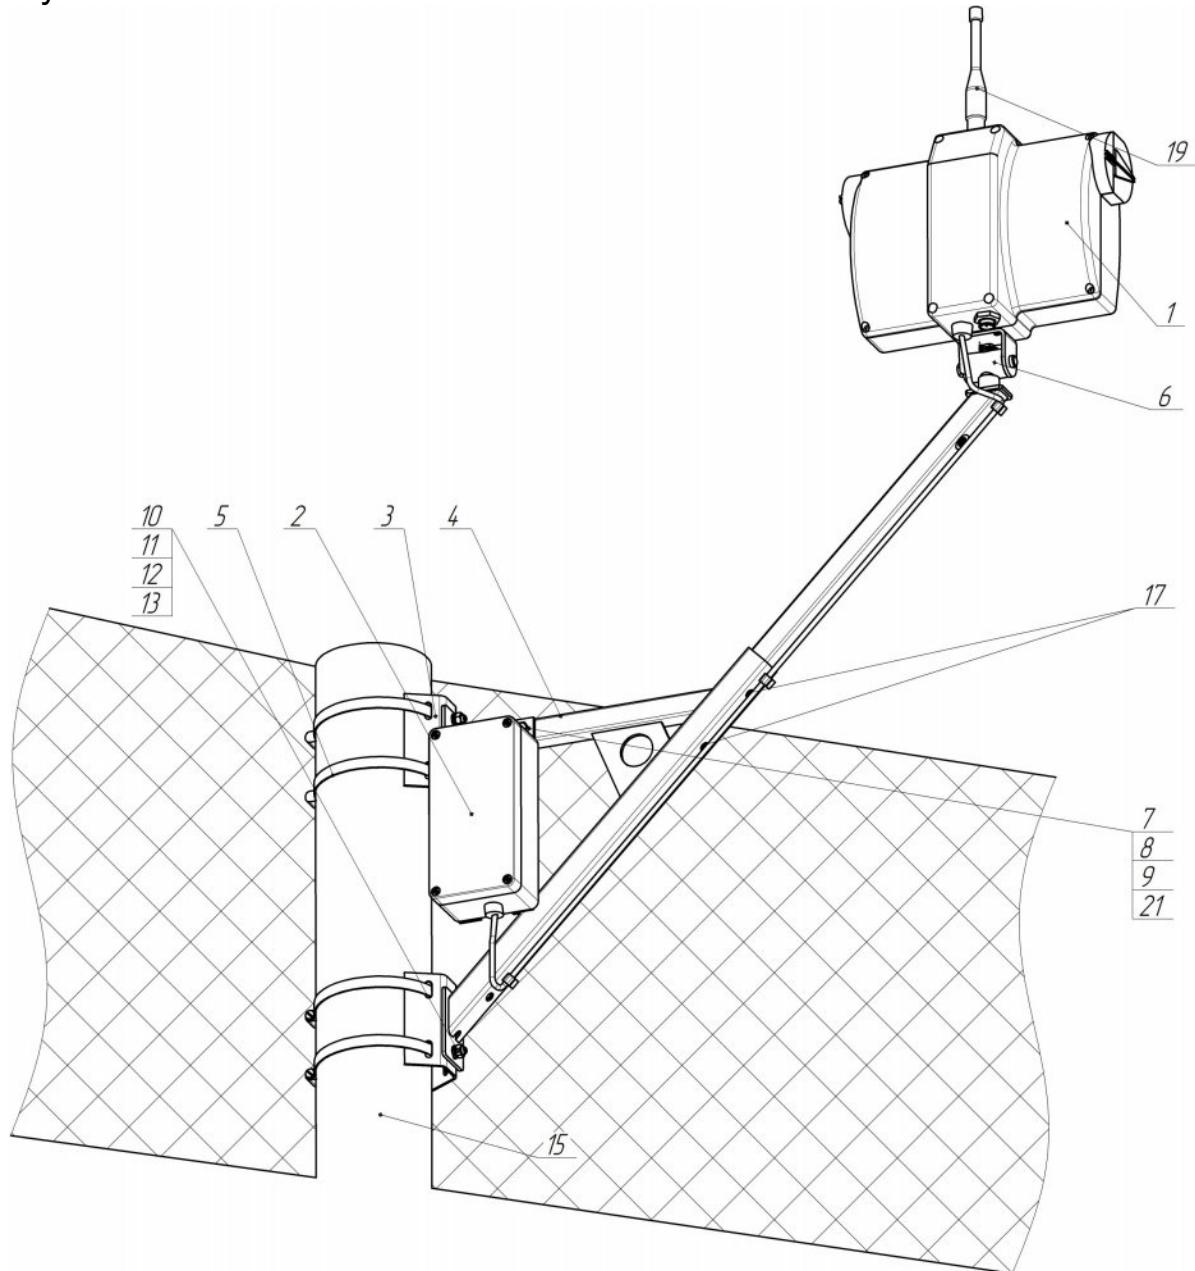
Способ крепления блоков на плоской поверхности
